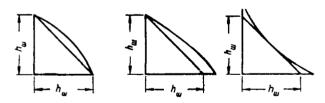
Схемы сварных швов  $h_{\rm m}$  — толщина шва
